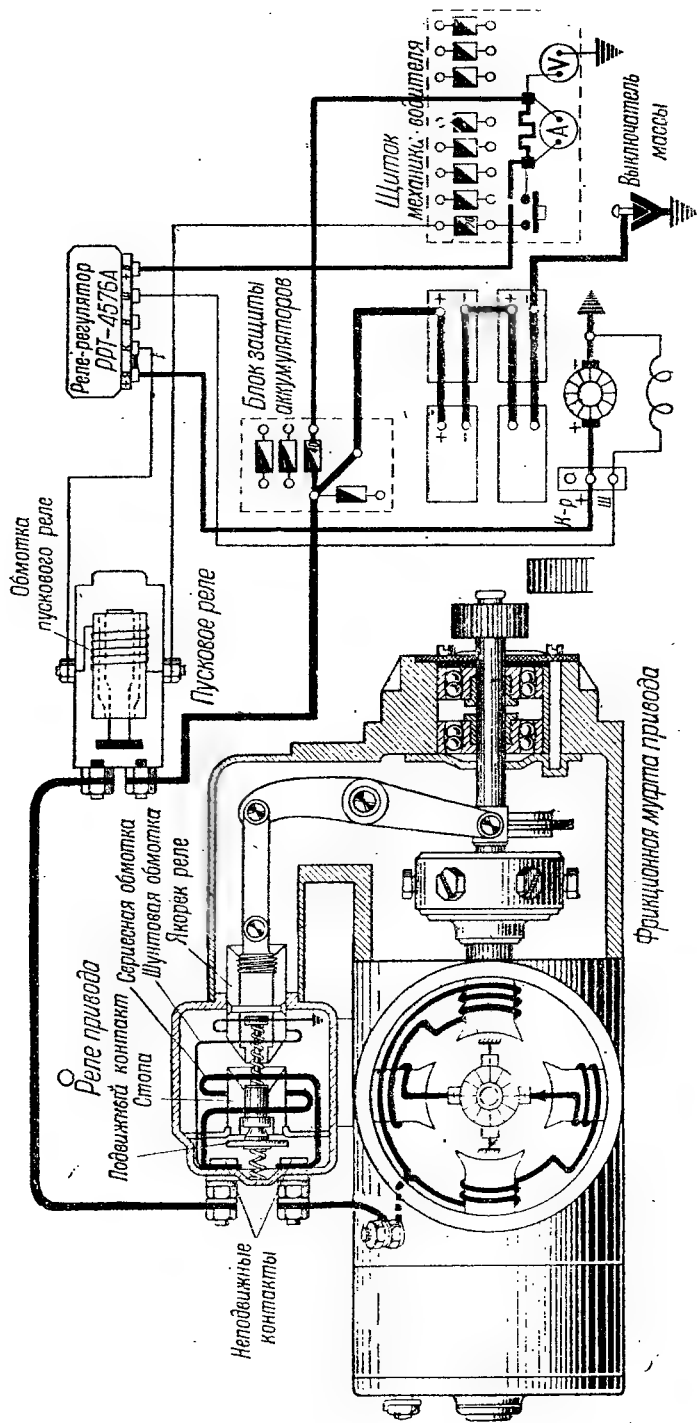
Схема соединений и исходное положение деталей стартера СТ-700 в танке Т-34
